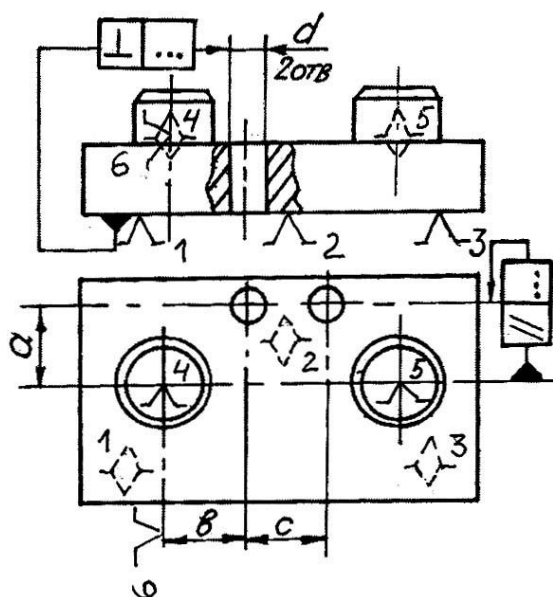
Схема базирования заготовки детали «Плитка»
